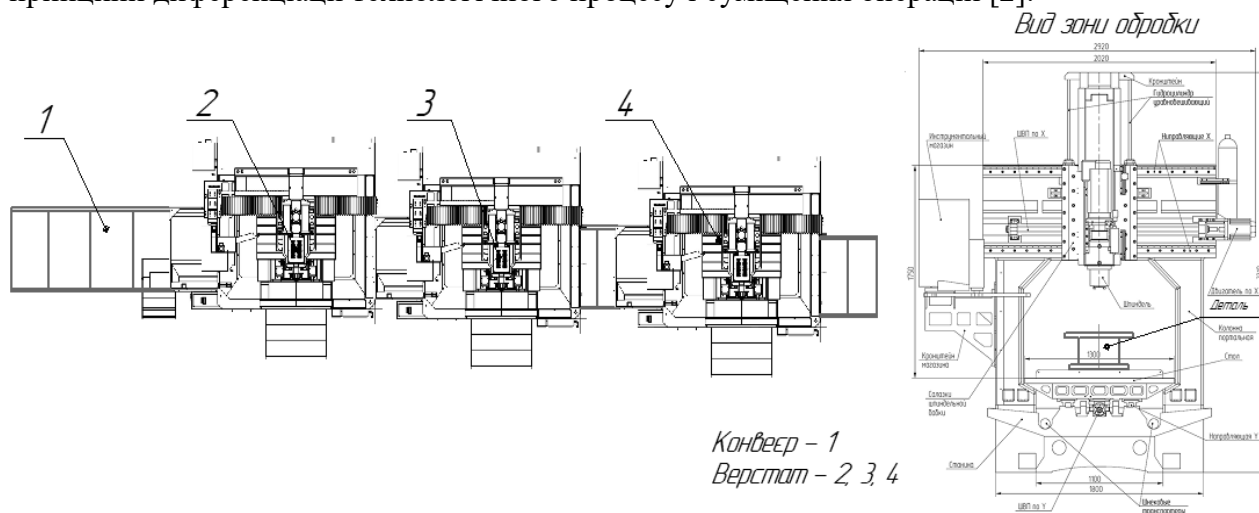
Компонувальна схема обробки деталі «корпус»
